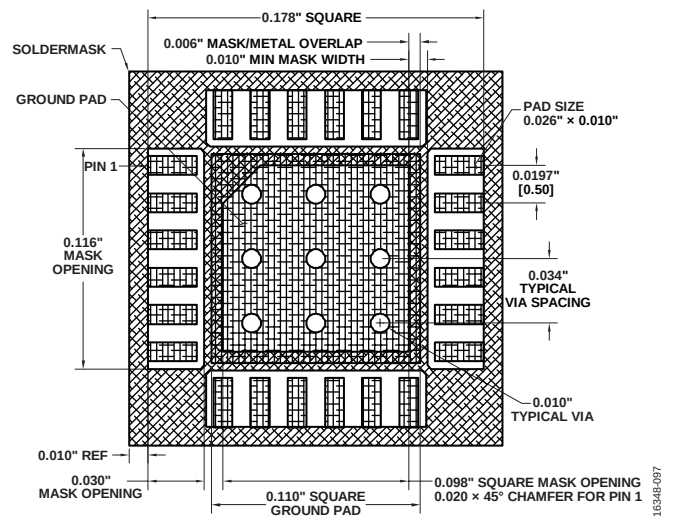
EV1HMC951ALP4 PCB ランド・パターンの寸法
